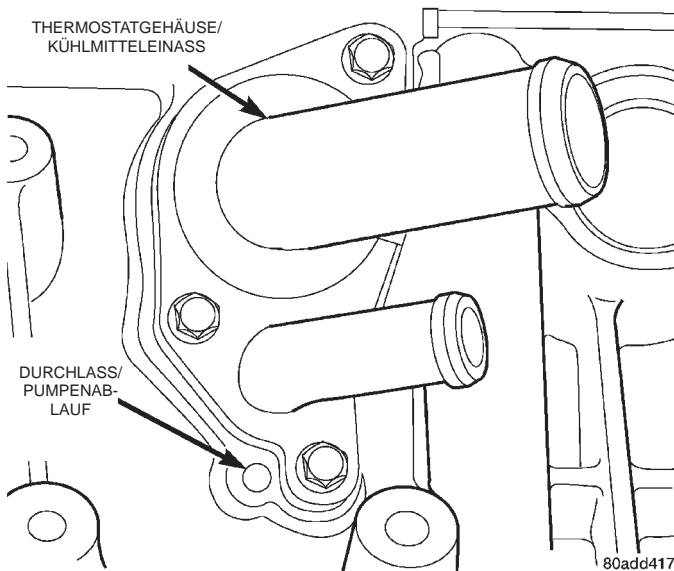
Durchlaß/Pumpenablauf—2.7L-Motor
